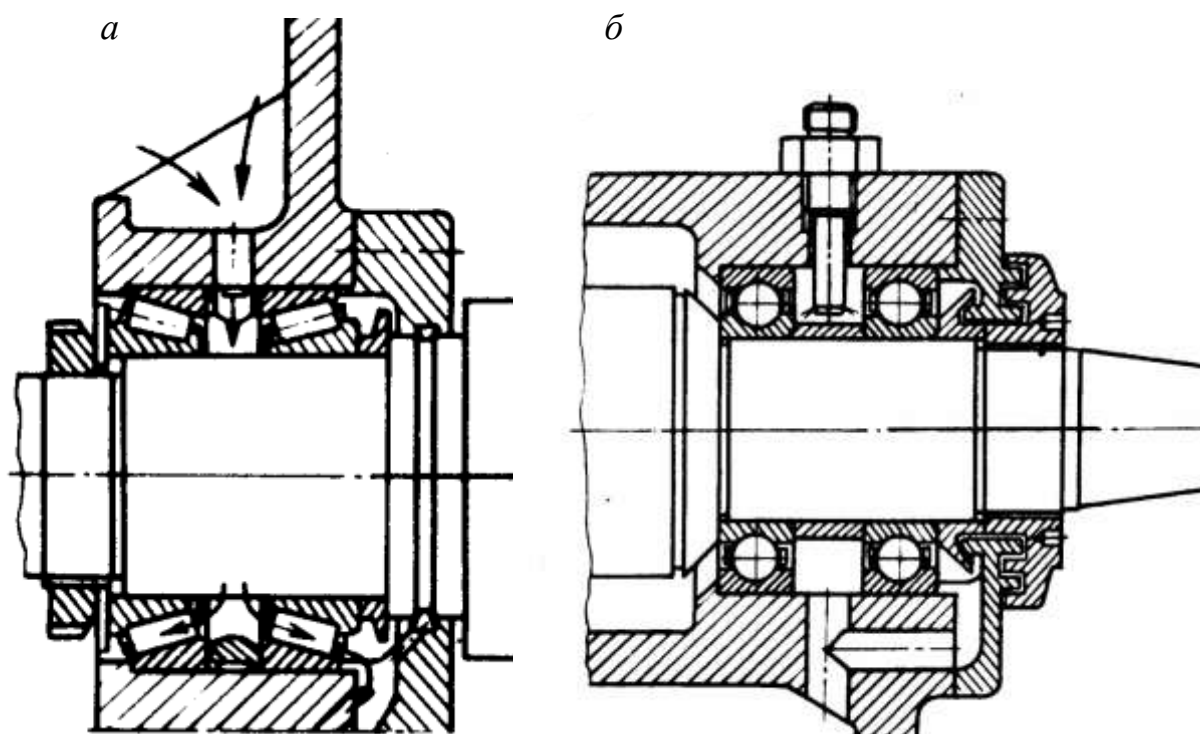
Варианты конструкции смазочных устройств, обеспечивающих:
